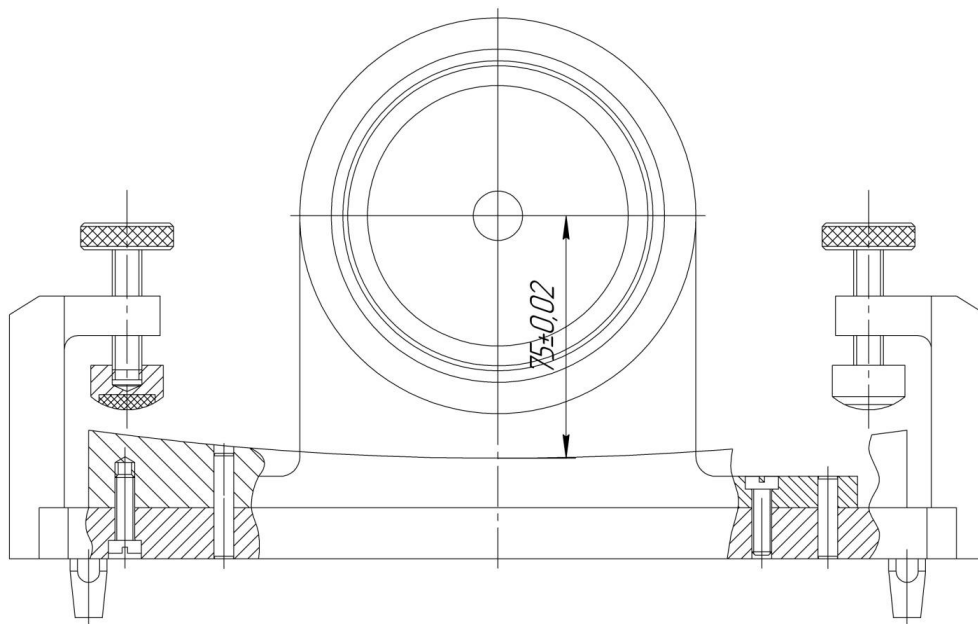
Приспособление для проверки радиуса заданного профиля
